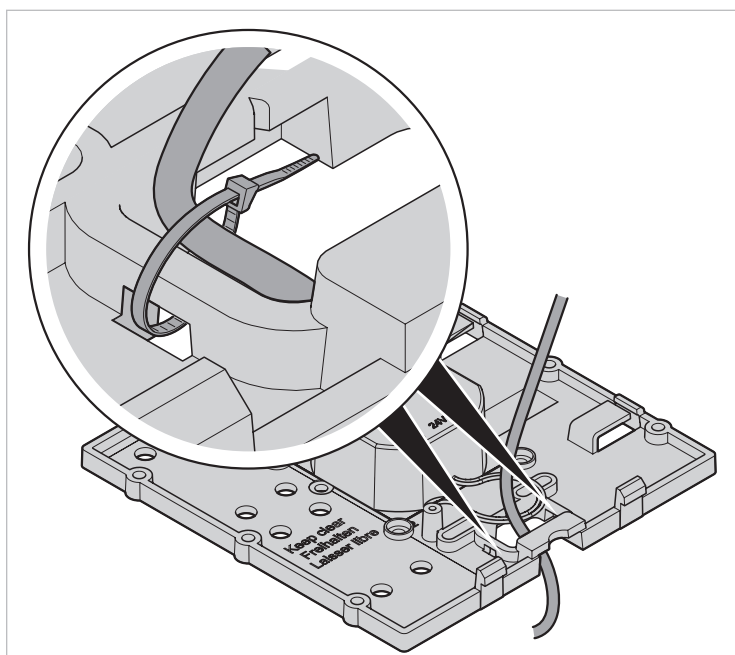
Kabel an der Universal-Montageplatte befestigen
